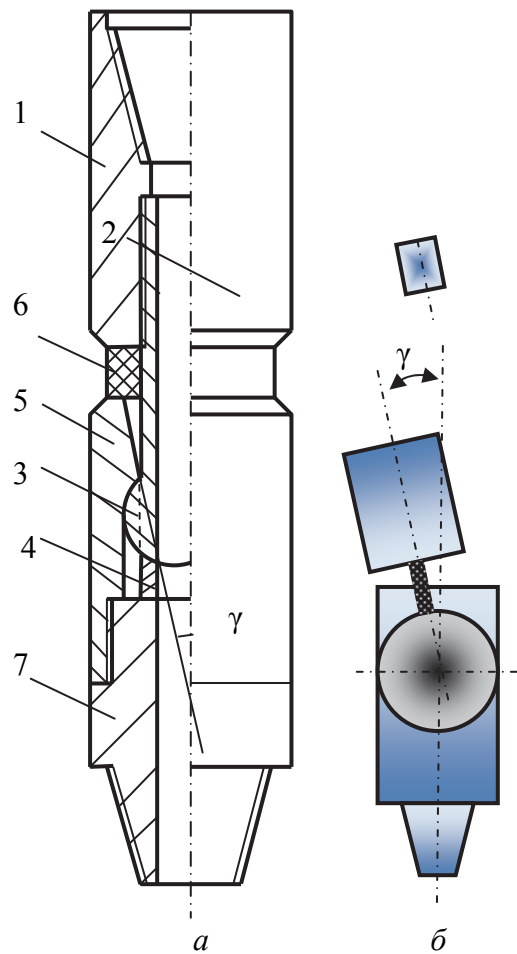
Устройство шлицевого шарнирного соединения (переходника) – (а) и схема, поясняющая существо работы шарнирного переходника (б)
